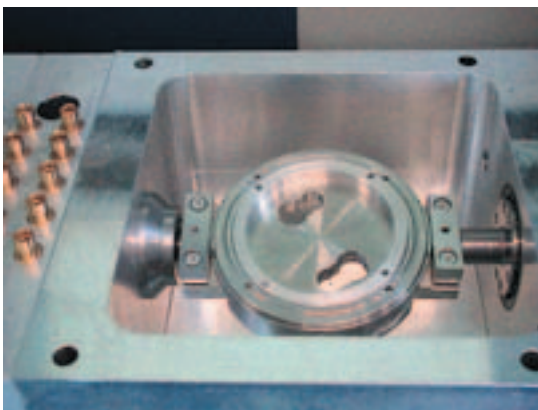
Fräsbecken der i-mes-Fräsmaschine.
